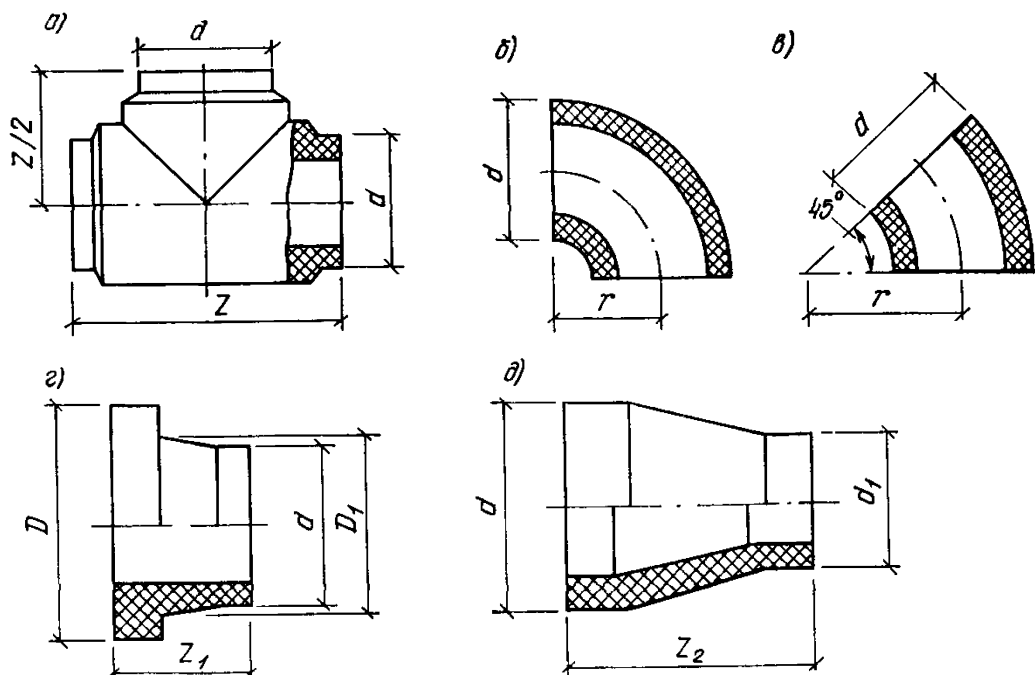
Соединительные детали из ПНД, изготавливаемые методами литья под давлением, прессования и намоткой:
